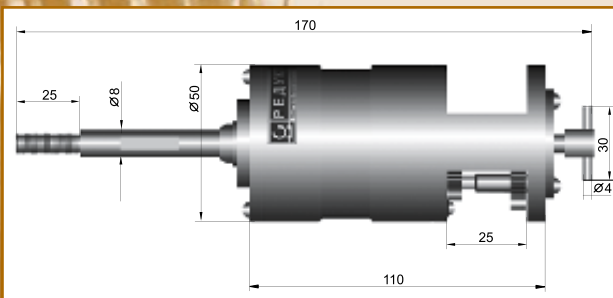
Габаритные размеры цилиндро-планетарного редуктора, радиус выходного водила 10,5 мм, передаточное число  $i = 346$
